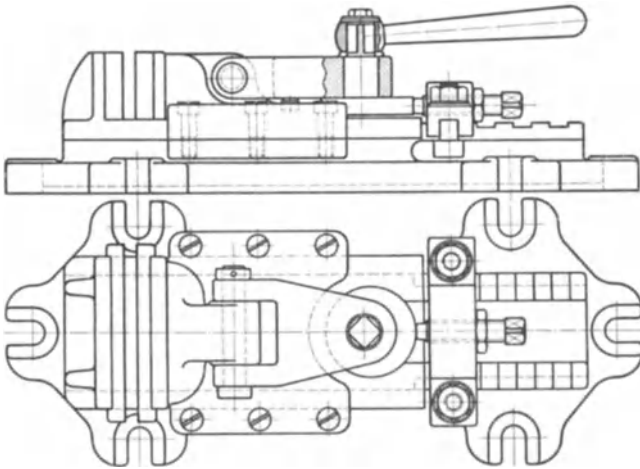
Maschinenschraubstock mit Schnellspanneinrichtung.
